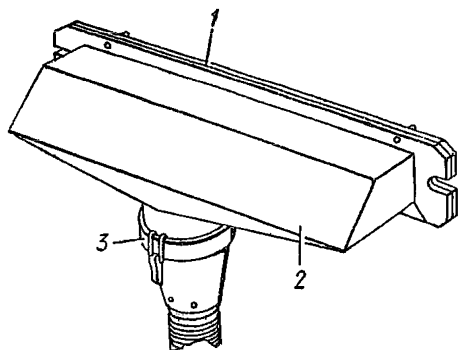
Наконечник к выпускному патрубку двигателя танка Т-72:
